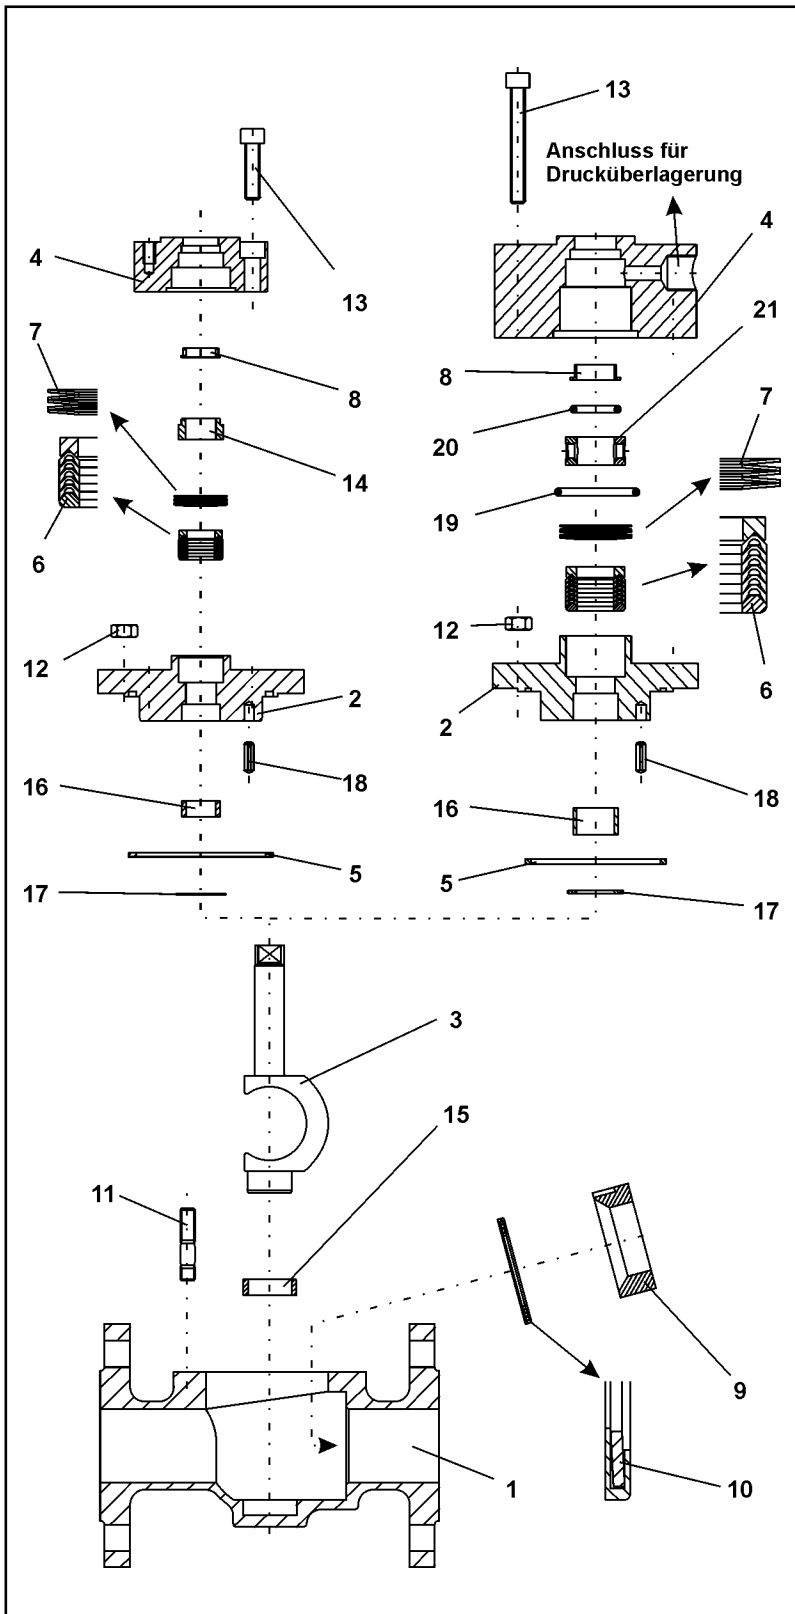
Explosionszeichnung des Drehkegelventils BR 23a
